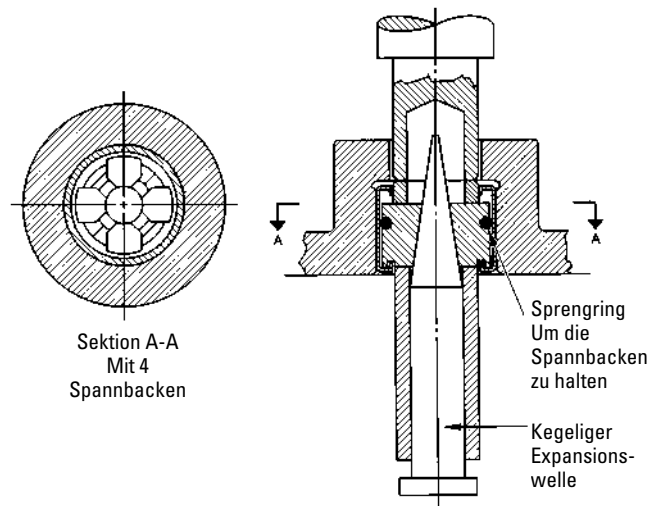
Demontage aus einem Gehäuse mit Anschlag
